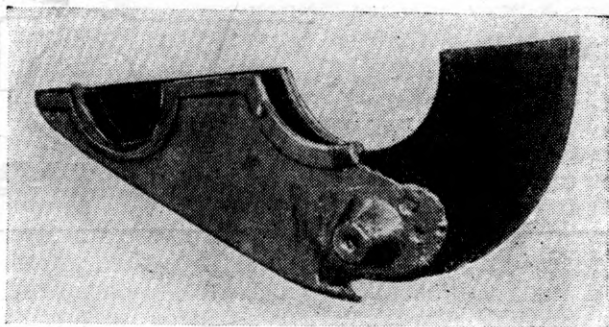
Нижняя половина поврежденного кожуха зубчатой передачи
